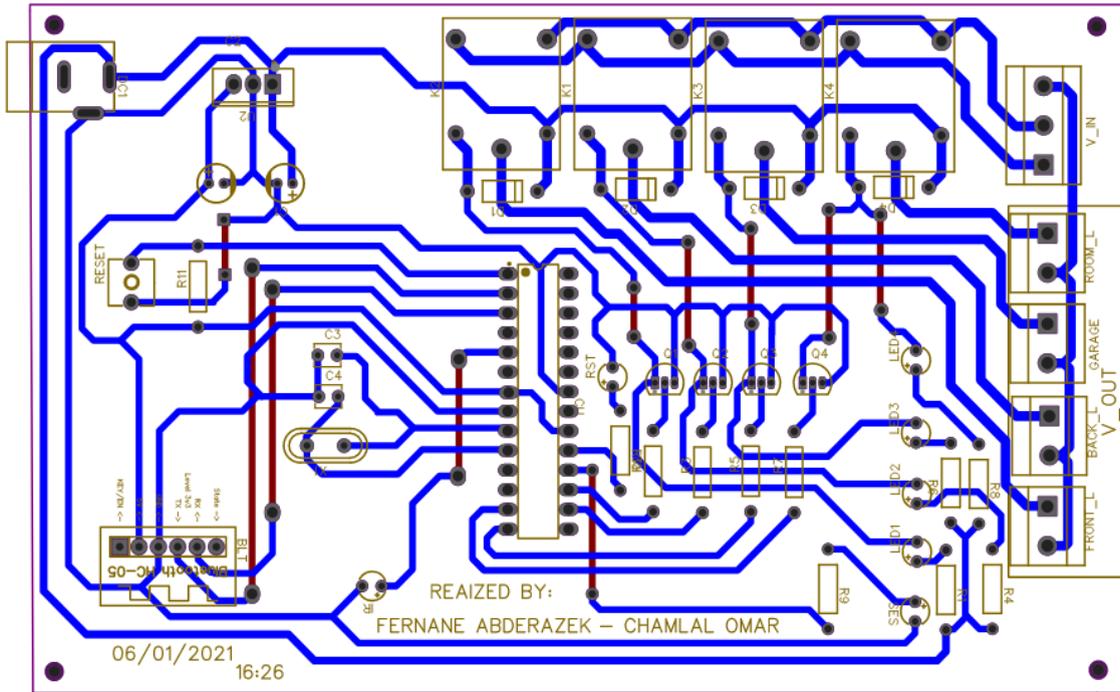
Carte PCB avec un Arrière-plan Blanc
